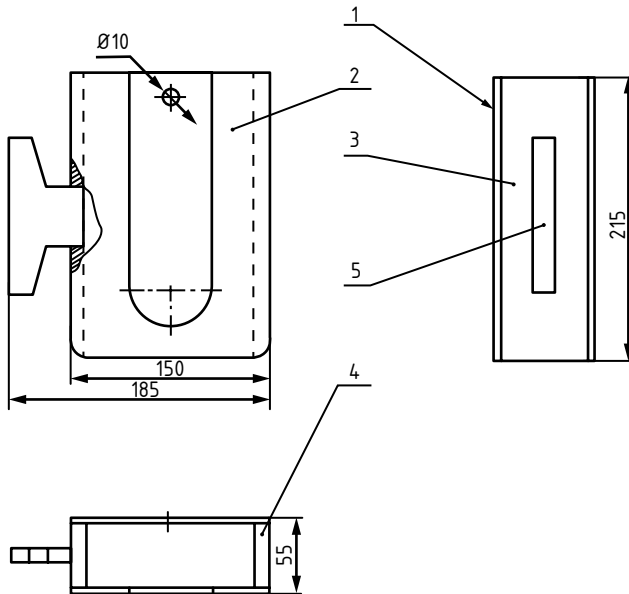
Plano de ensamble del portaplancha eléctrica
